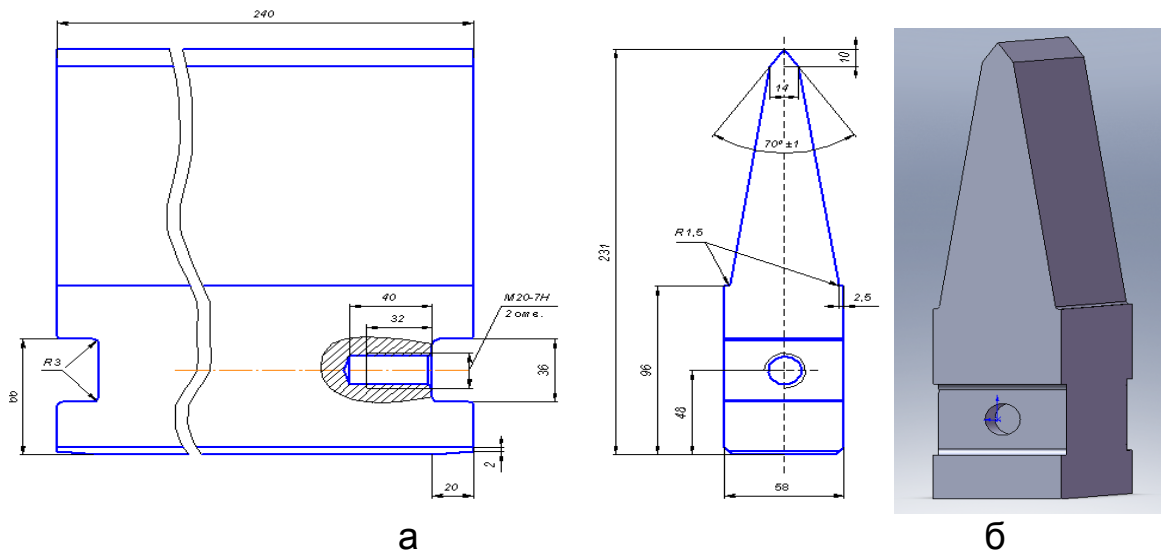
Чертеж (а) и 3D-модель (б) унифицированного ножа для резки квадратных заготовок 160x160, 200x200, 240x240 мм с углом клиновидности 70 (5ХВ2С)
